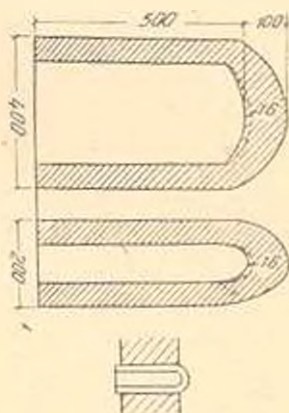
Схема стальных электродов, их разъедания с наружной стороны и расположения в стене ванны печи.
